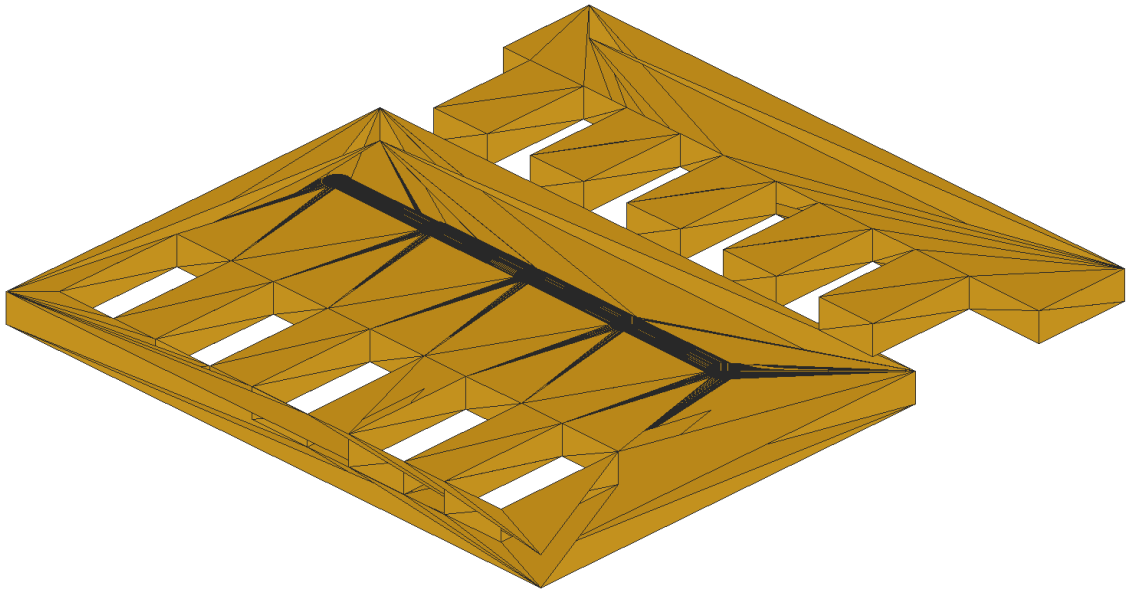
FDM tolerance coupon — 실제 측정 전 모든 print fit은 provisional
